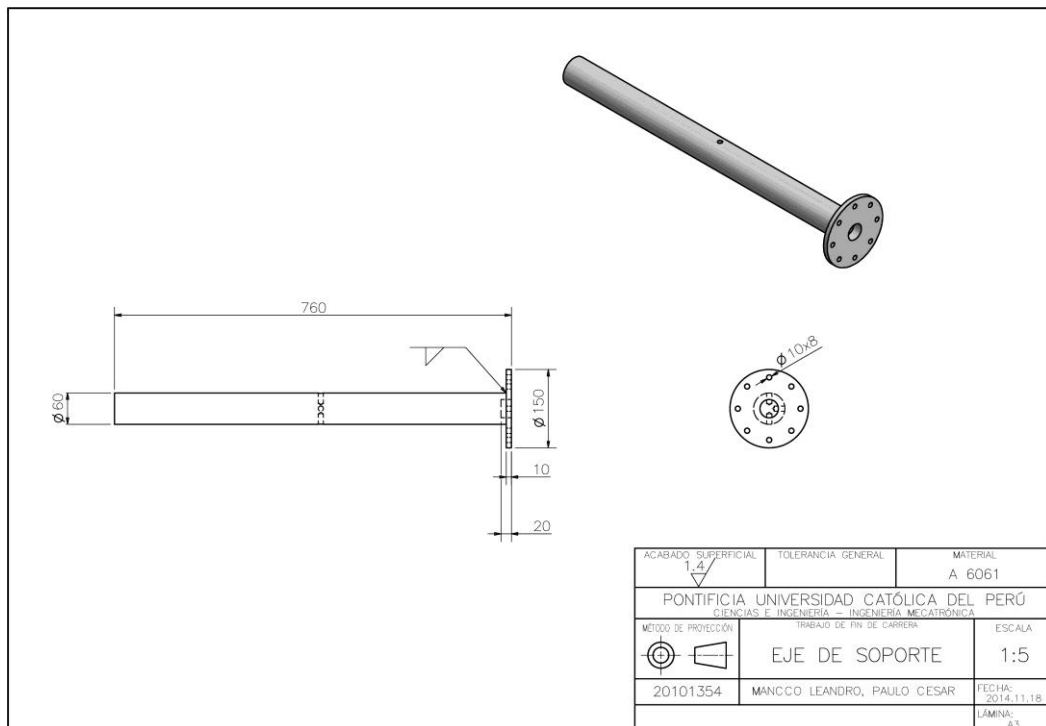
Plano de despiece de eje de soporte de transmisión del torque del tornillo sin-fin corona al panel solar
